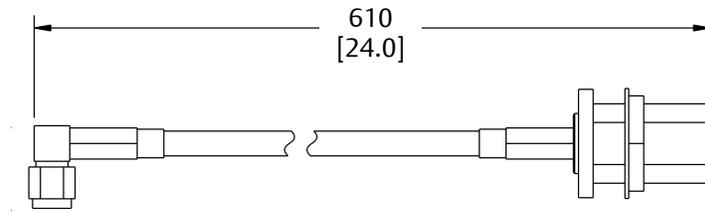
Dimensões do cabo adaptador SMA para N-Type
